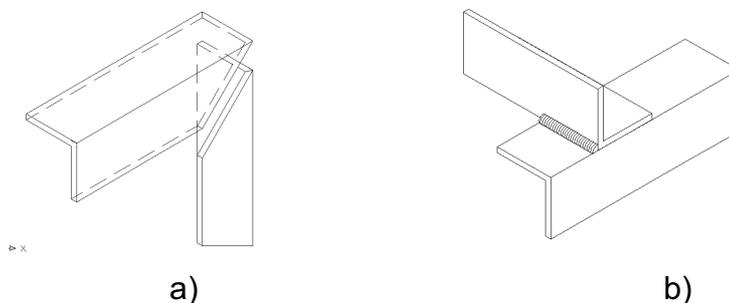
Tipos de juntas utilizadas para la elaboración de la estructura. a) Soldadura sobre bordes rectos(a tope), b) soldadura angular
